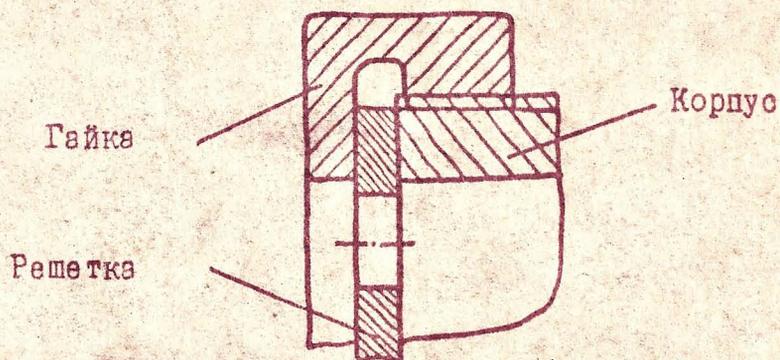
Крепление решетки увеличенного диаметра к корпусу
